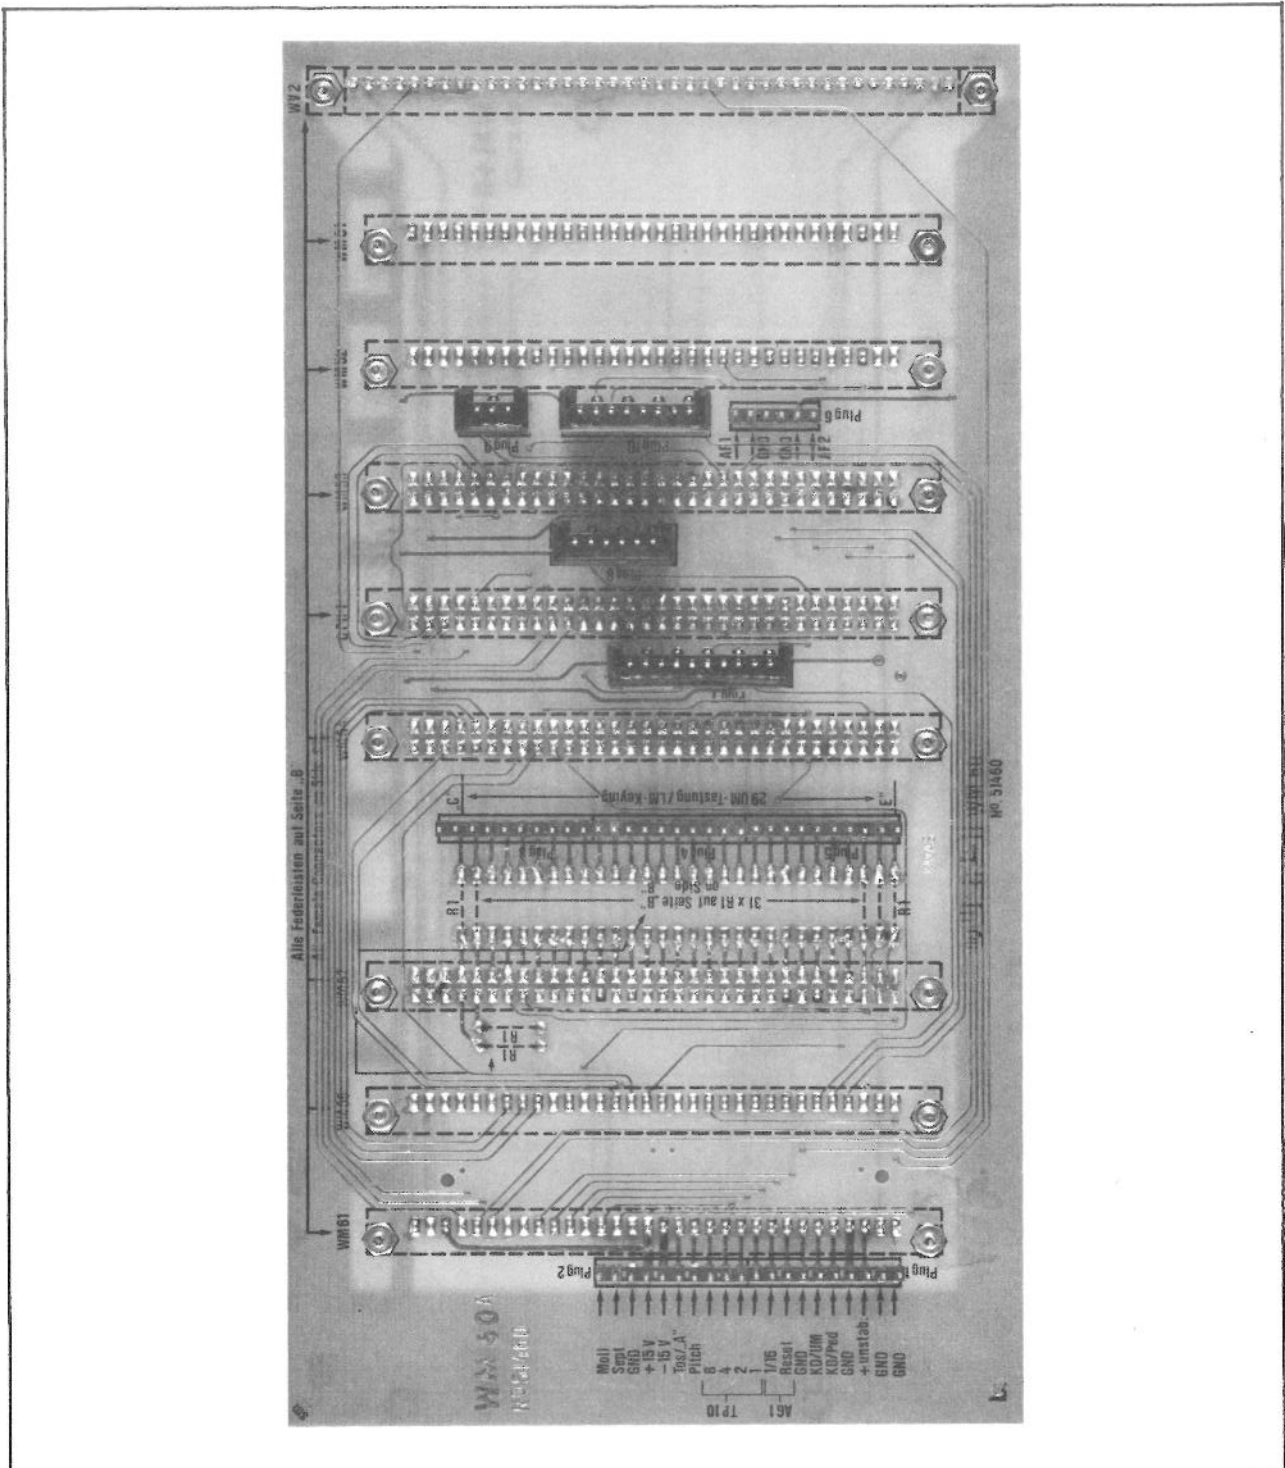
Fertig bestückte Grundplatine WM 60, A-Seite
